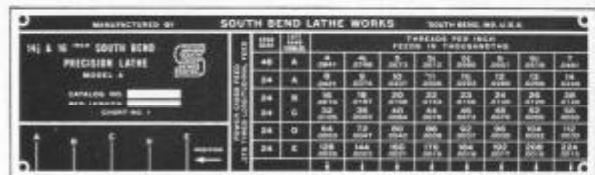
B. Placa índice para torno con engranajes de cambio rápido
